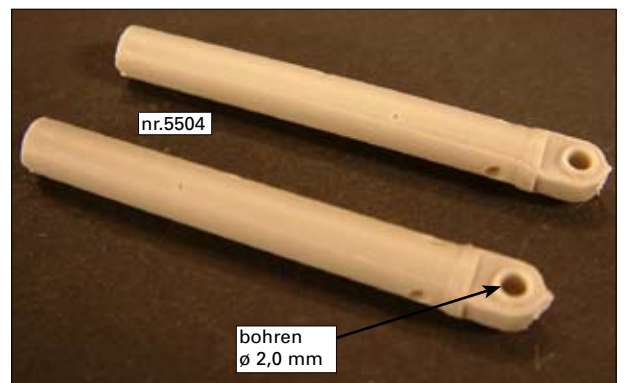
Unbearbeiteter neben einem bearbeiteten Zylinder
